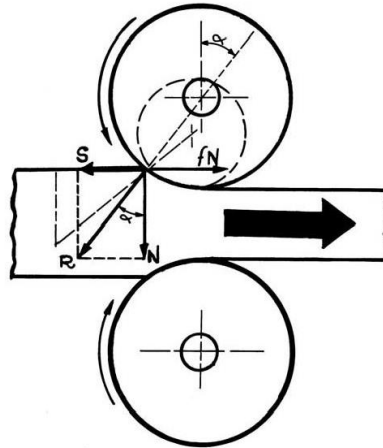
1.- Fuerzas de Rodillos Laminadores.
